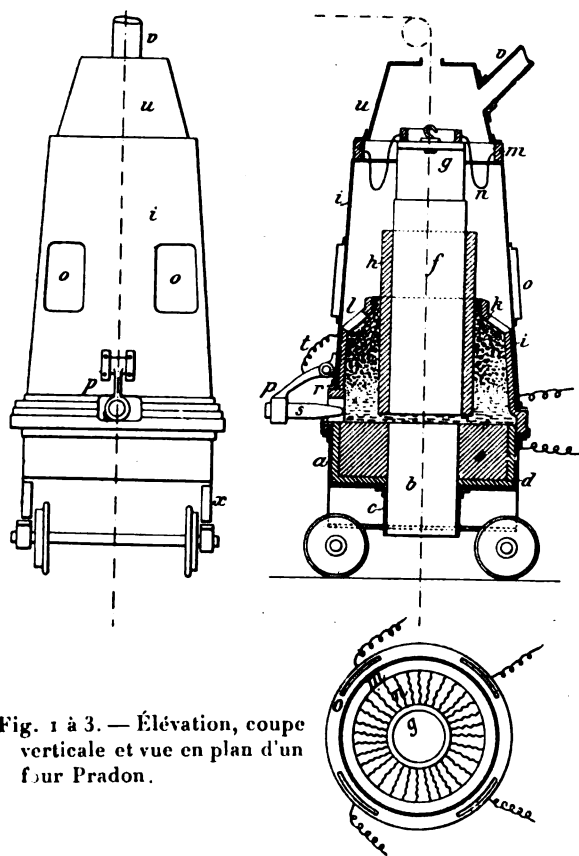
à 3. — Élévation, coupe verticale et vue en plan d'un four Pradon.
